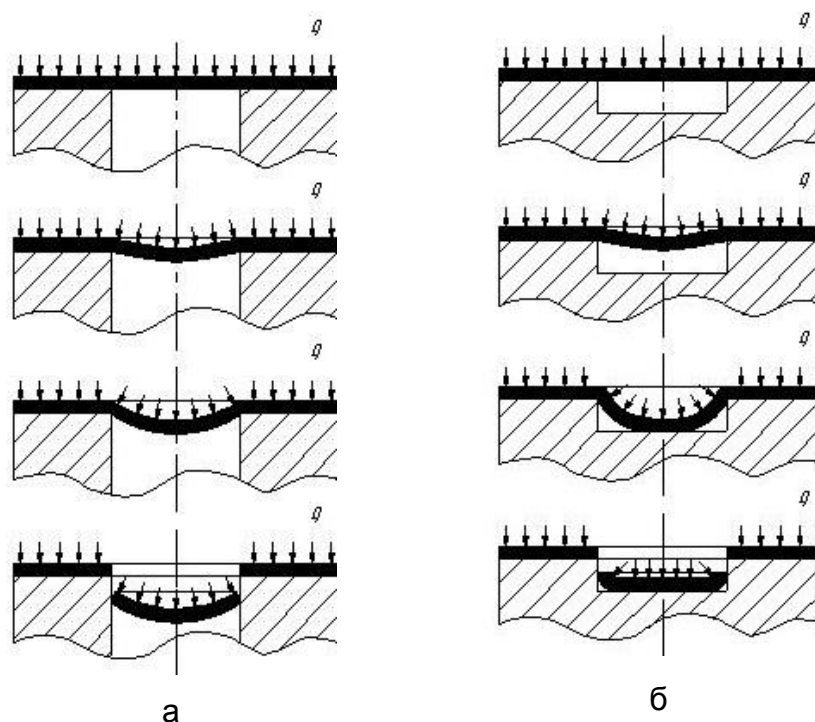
Схемы пробивки отверстия в листовой заготовке
